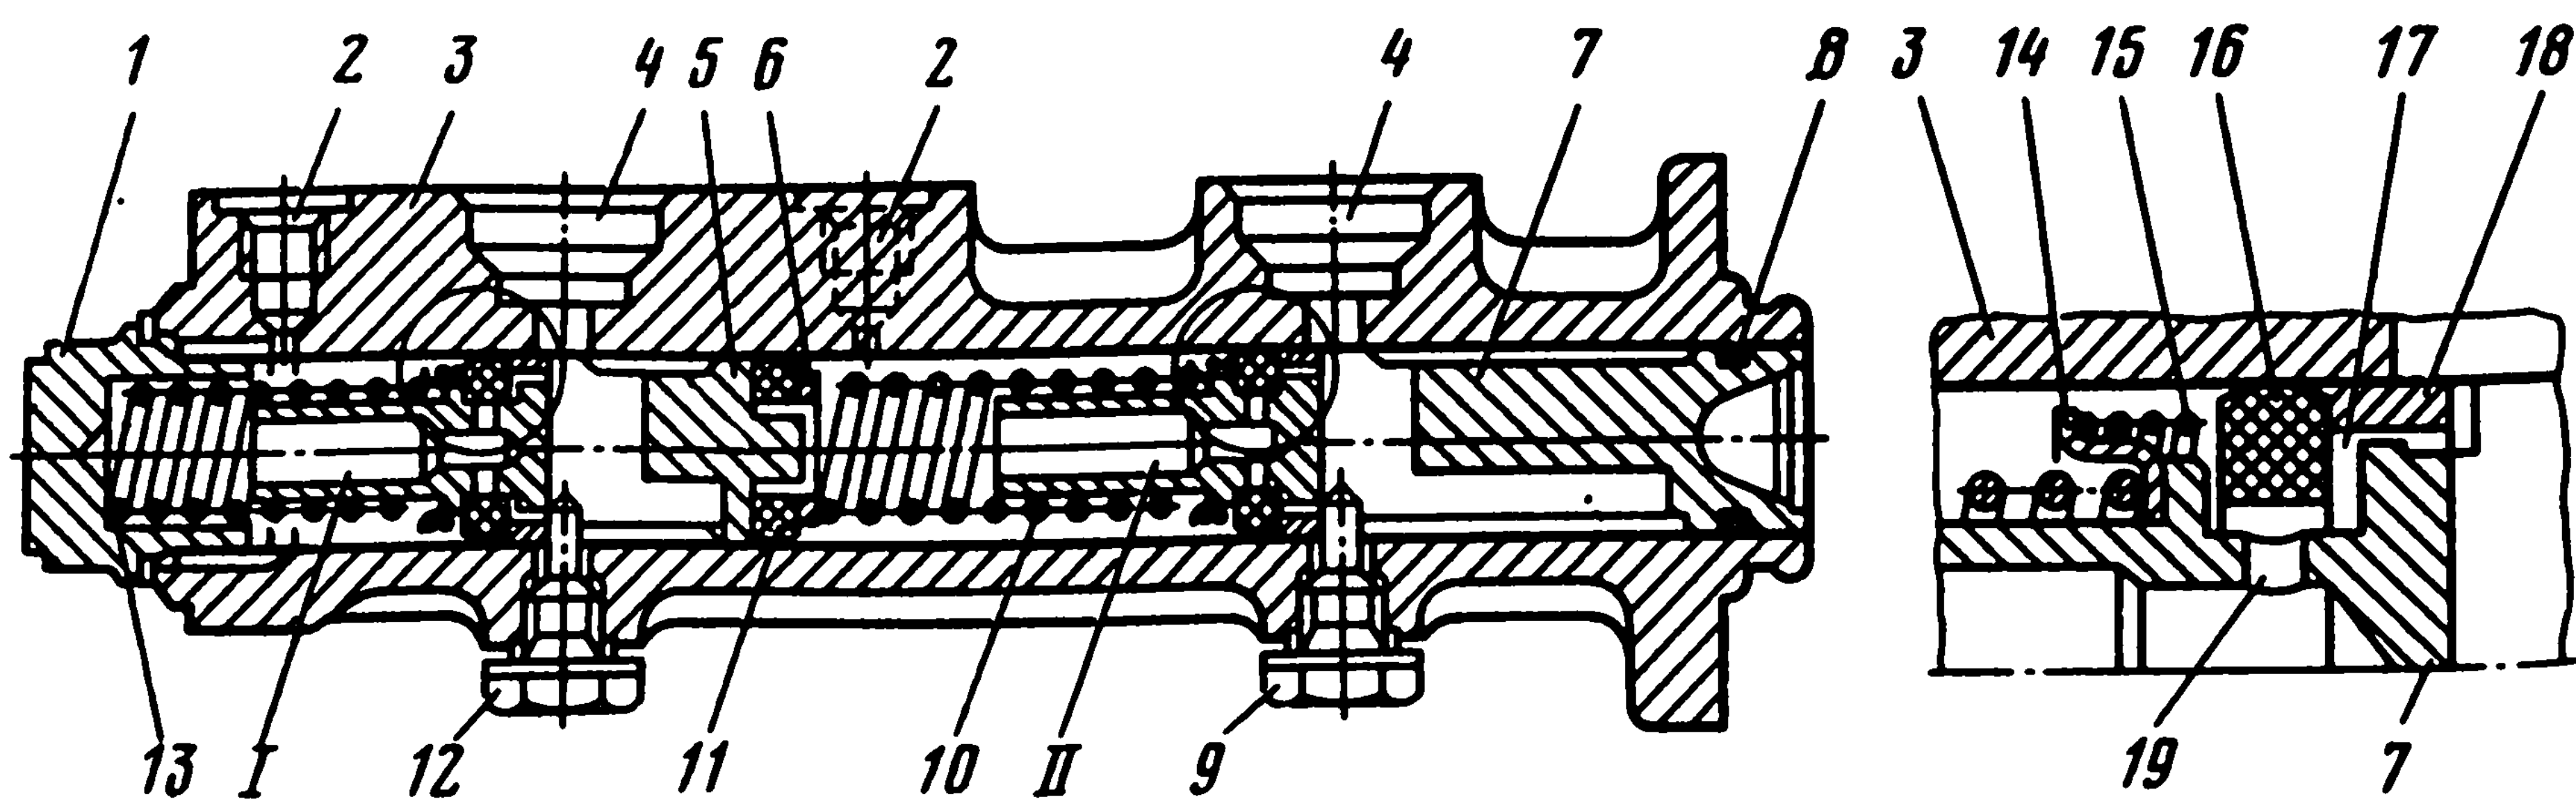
Главный тормозной цилиндр автомобилей ВАЗ-2121 и ВАЗ-2105
